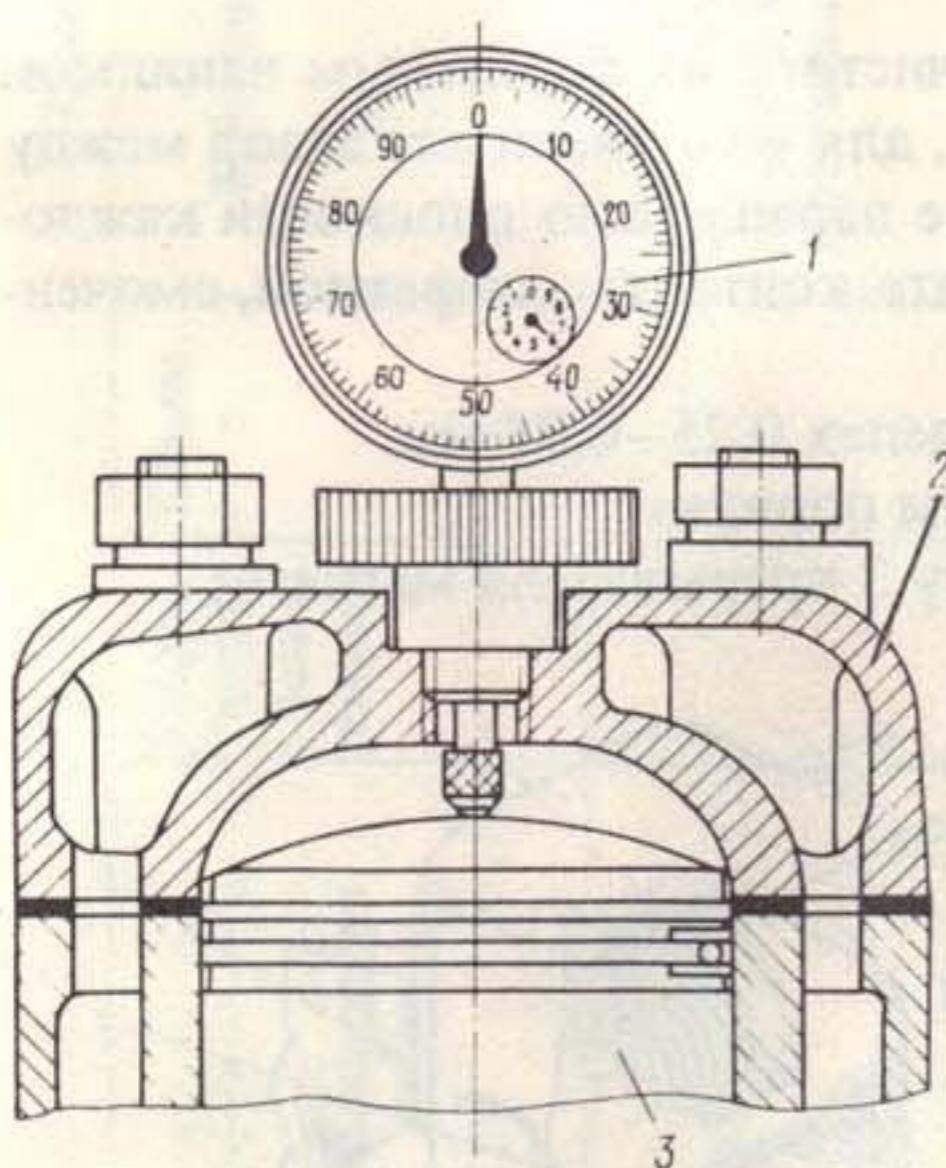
Определение положения поршня пускового двигателя в ВМТ:
